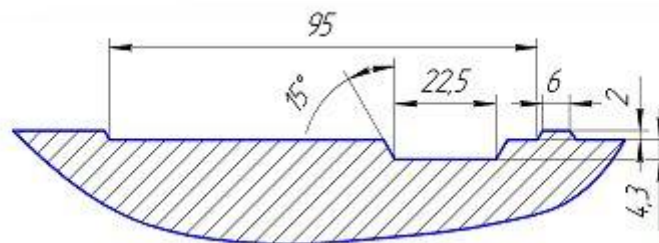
Підготовка поверхні під наплавлення при ремонті ущільнюючої поверхні корпусу реактора
